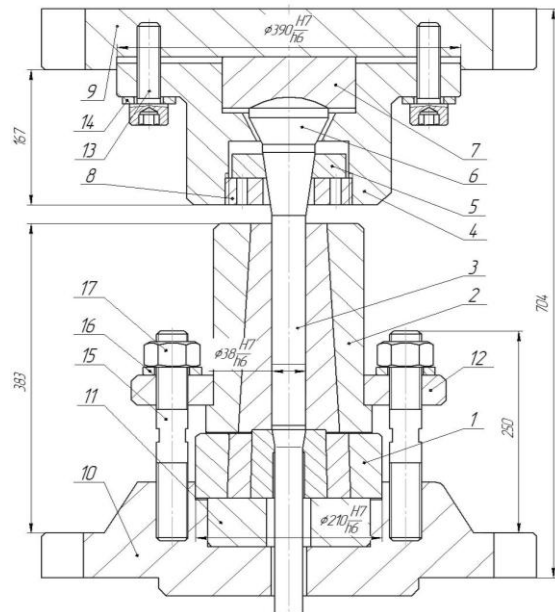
Конструкция штампа для прямого выдавливания по схеме «заготовка за заготовкой»
